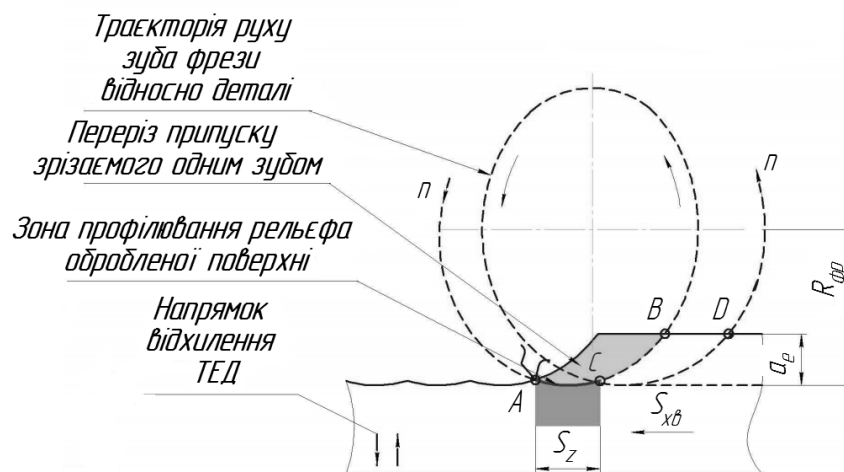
Формування профілю обробленої поверхні при зустрічному фрезеруванні ТЕД однозубою фрезою
